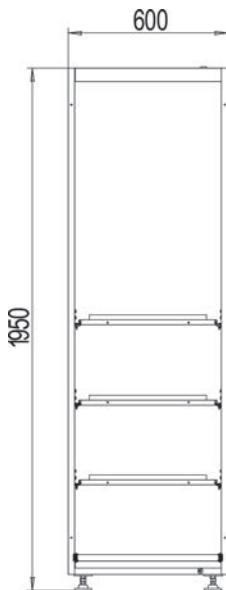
Габаритный чертеж стеллажа аккумуляторного 1950x600x600
